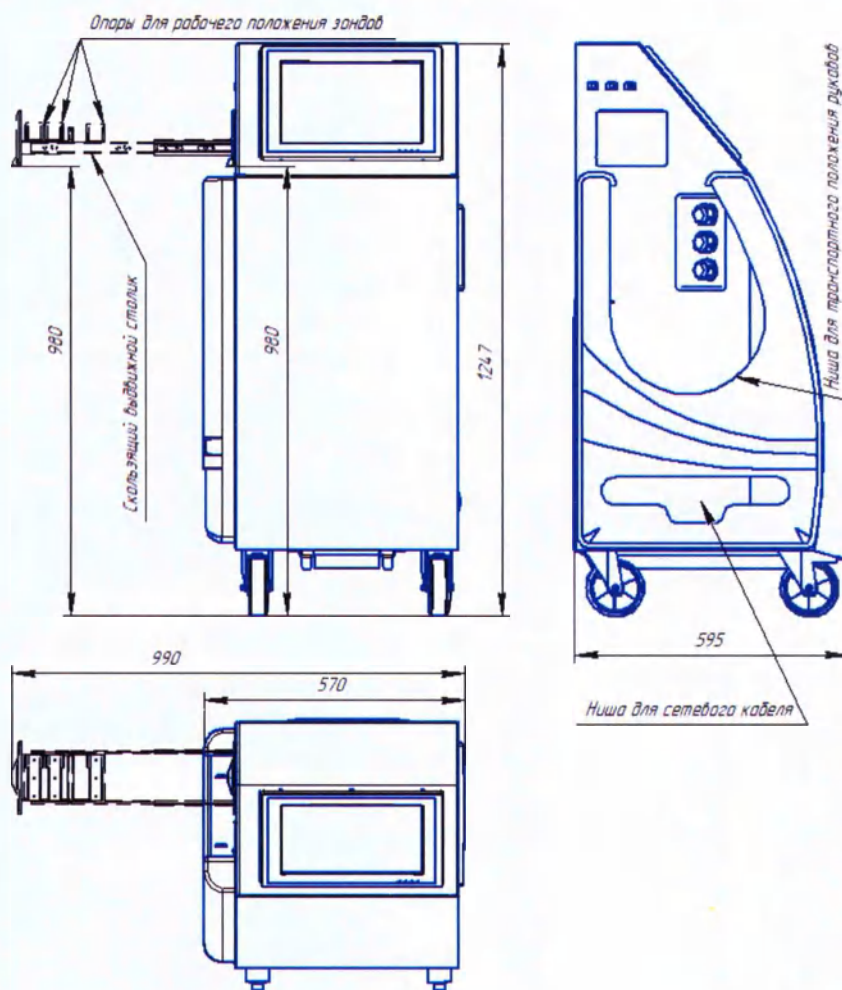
Внешний вид и габаритные размеры установки в рабочем положении.
